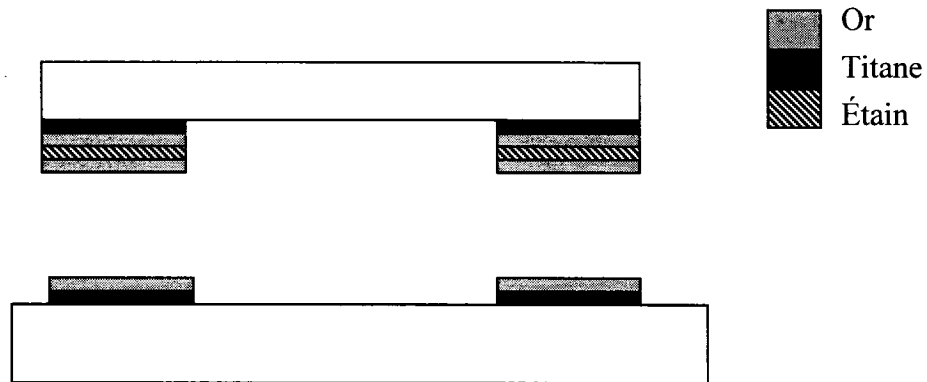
Technique de soudure eutectique multicouche
